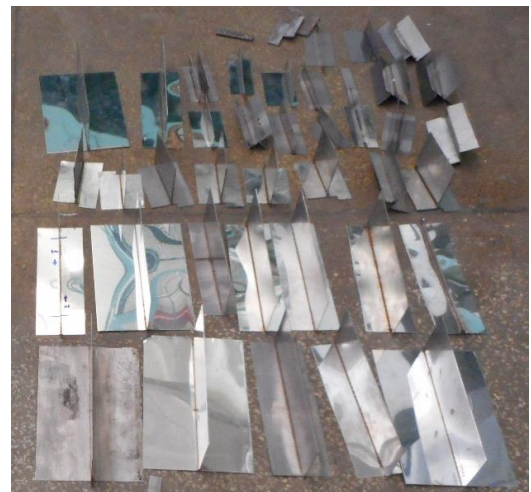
Образцы тавровых соединений, сваренные лазерной сваркой
